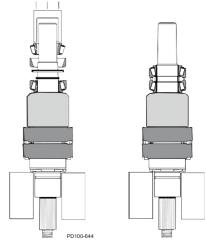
Montaje del rodamiento trasero con rodillos en cinta
